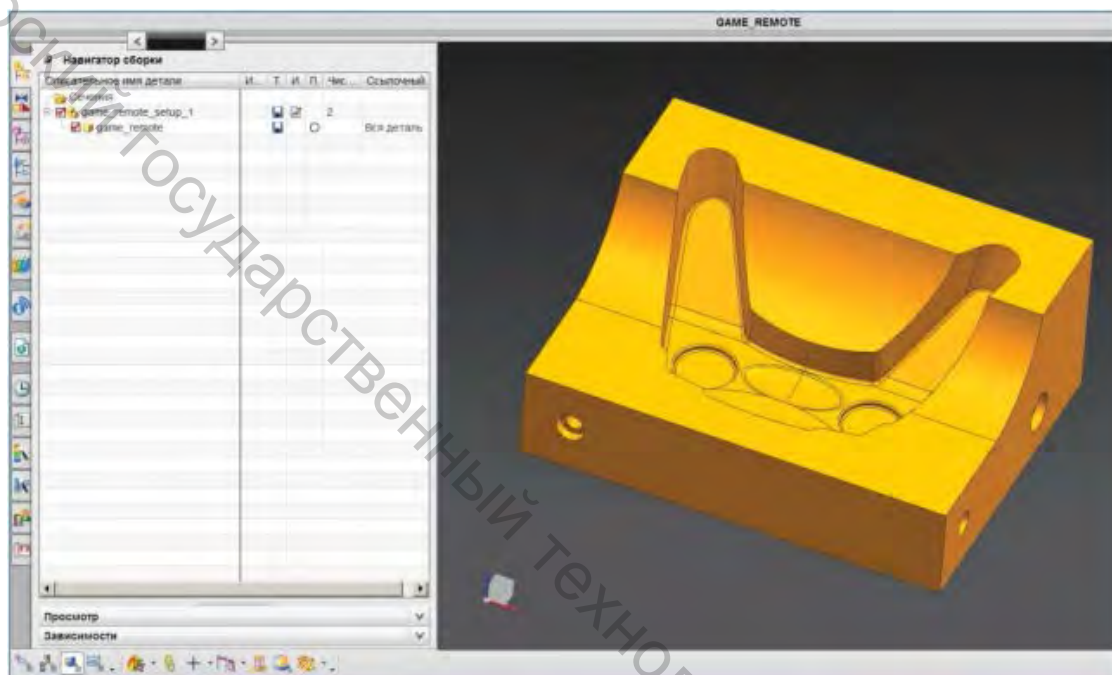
Отображение нового проекта для фрезерной обработки детали
